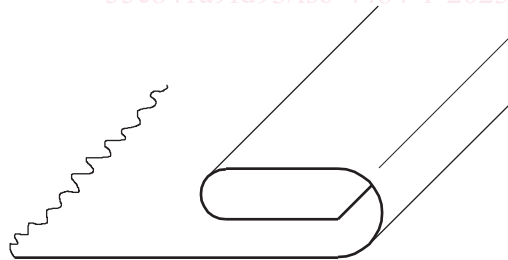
Ourlet enroulé doublé, type 6.03.01
